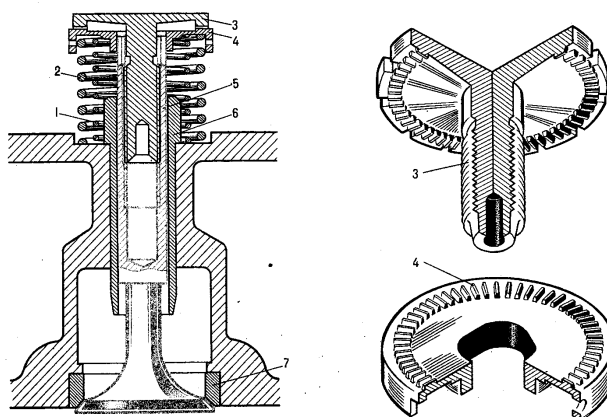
Клапан высокооборотного дизеля с верхним расположением распределительного вала
